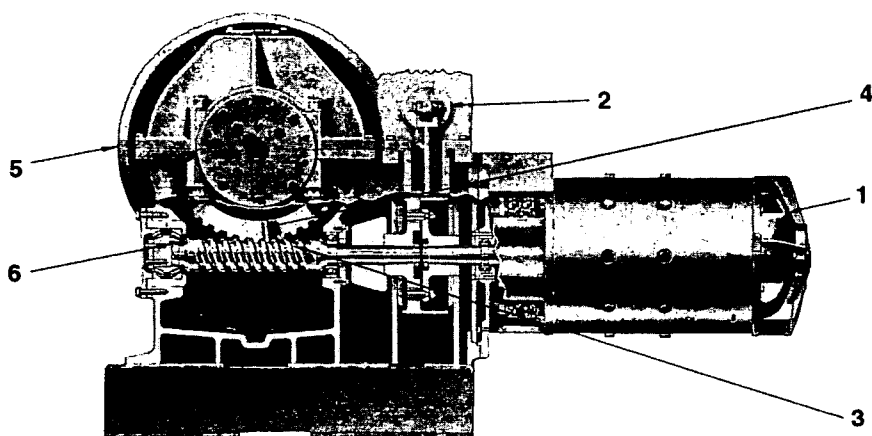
Типичная конструкция редуктора с нижним червяком (Otis Elevator Co.):
